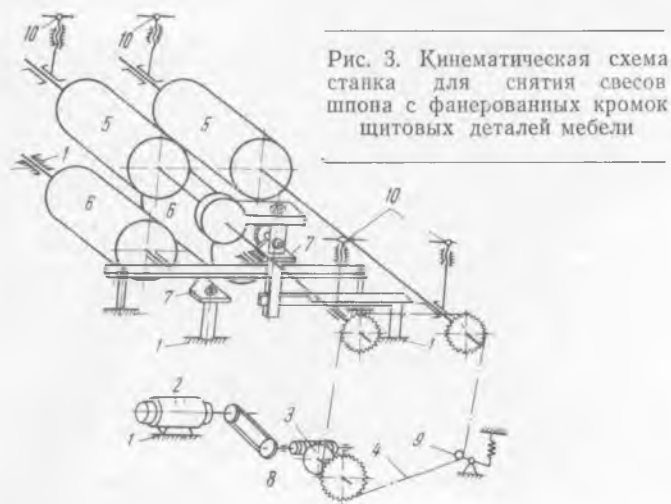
Кинематическая схема станка для снятия свесов шпона с фанерованных кромок щитовых деталей мебели
